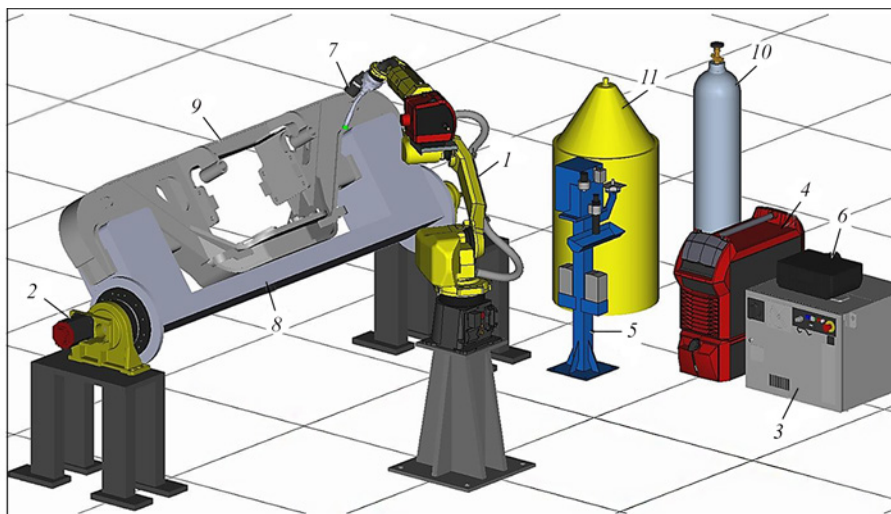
Макет робототехнічної системи для автоматизованого зварювання бокової рами візка вантажного вагона, створений у пакеті моделювання Fanuc Roboguide
